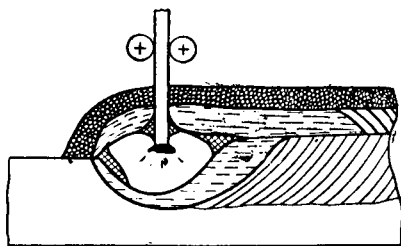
Схема процесса сварки под флюсом с выделением (штриховка крестом) его активной части, наиболее полно реагирующей с металлом
